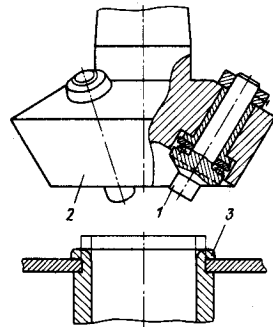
Отбортовка роликовой вальцовкой: 1 — ролики; 2 — корпус головки; 3 — деталь
